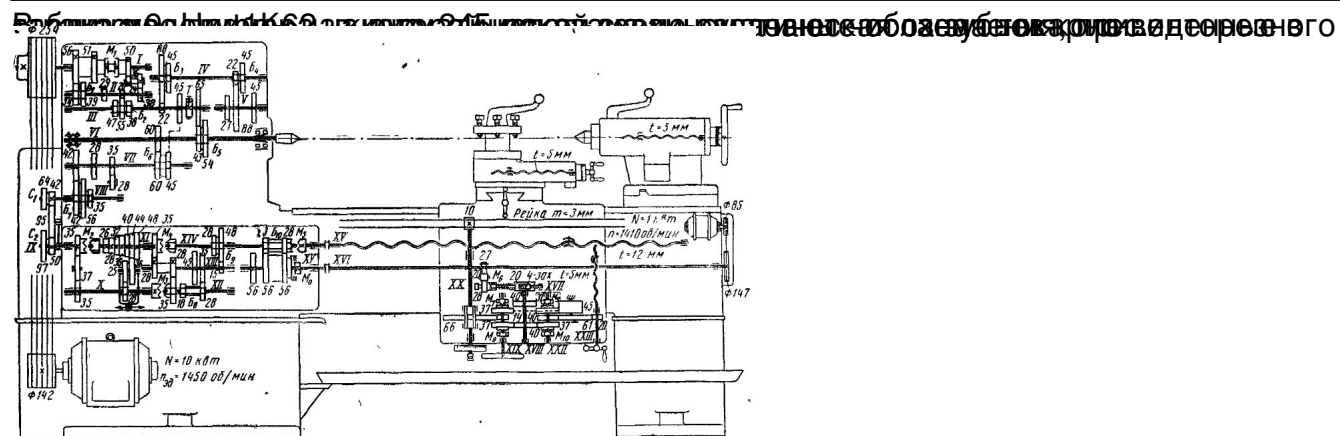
Кинематическая схема токарно-винторезного станка модели 1К62
